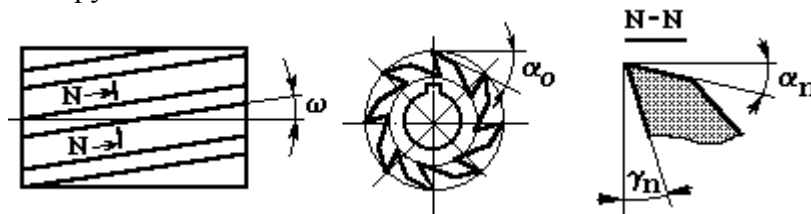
Геометрические параметры режущей части цилиндрической фрезы
